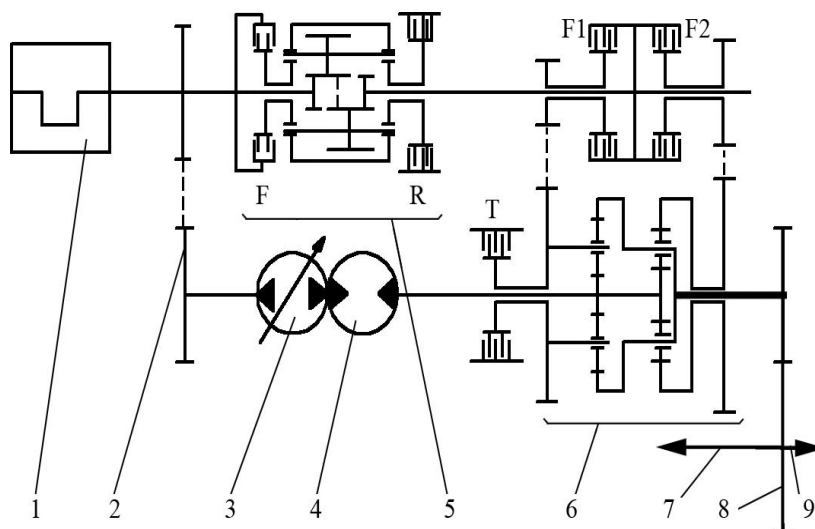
Кинематическая схема трансмиссии мотовоза МТ-1: 1 – дизель; 2 – входной редуктор; 3 – блок управляемых гидронасосов; 4 – гидромотор; 5 – реверсивное устройство; 6 – коробка передач; 7 и 9 – приводы осей; 8 – раздаточная коробка
